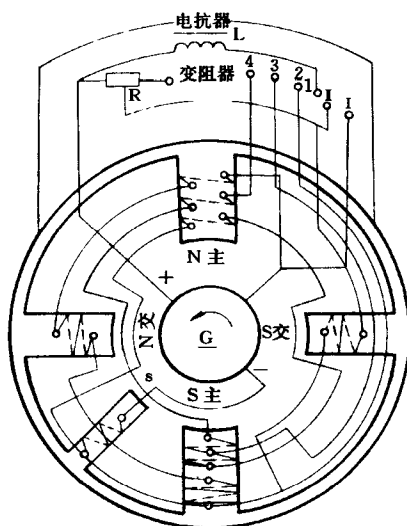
AX1-165 型直流焊接发电机电气线路图
